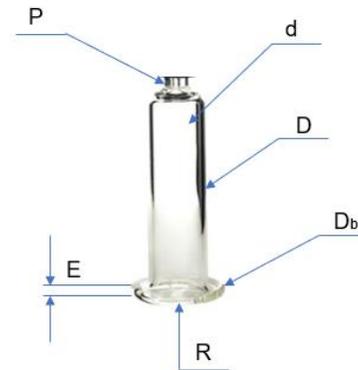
Partes a inspeccionar en la Jeringa de insulina
